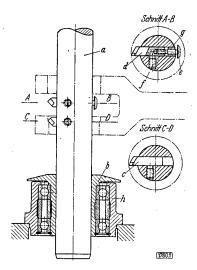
Feinbohrstange a Bohrstange, b Kugellagerbüchse, c und d Drehmeißel, c Stellschraube mit Differentialgewinde, f Klemmschraube, g Paßstück, h Kugellagerführung
